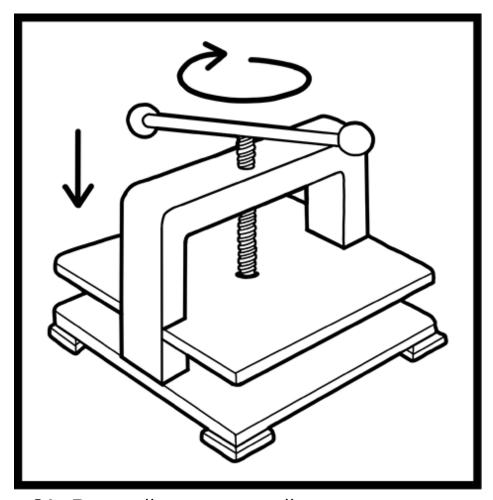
Винтовой пресс: устройство, что используется и в печатном деле, и в изготовлении вина, но не в одно и то же время
